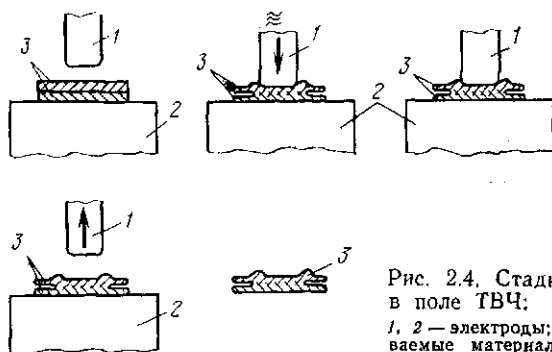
Стадии сварки в поле ТВЧ:
